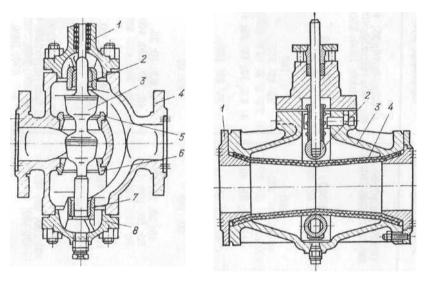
Двухседельный регулирующий орган: /— верхняя крышка; 2, 7— направляющие втулки; 3— затвор; 4— корпус; 5— верхнее седло; 6— нижнее седло; 8— нижняя крышка
